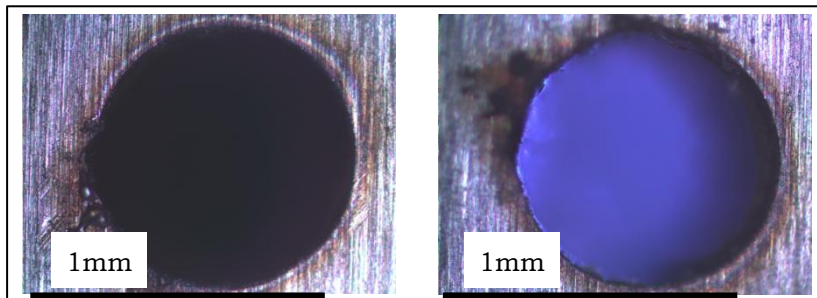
Taladrado láser por trepanado. Izq.) Test T11 Dcha.) Test T25
